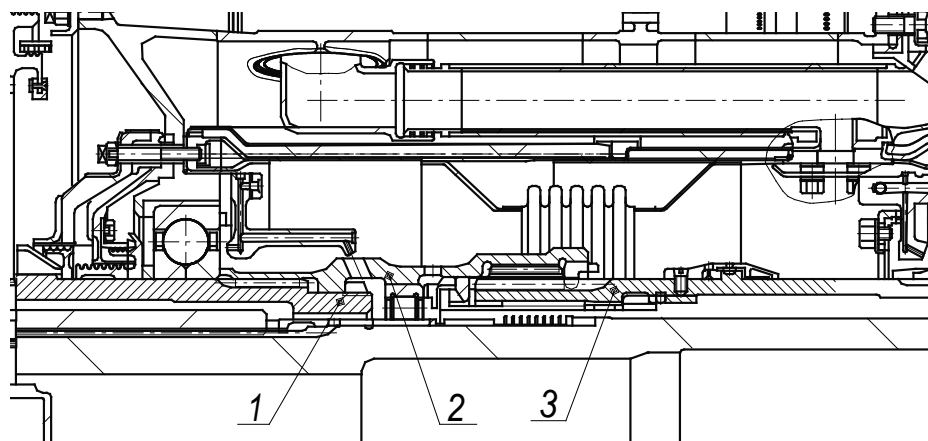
Соединение ротора компрессора и турбины ВД шлицевой муфтой в ТРДД ПС-90А: 1 – вал ротора компрессора ВД; 2- соединительная шлицевая муфта; 3 – вал ротора турбины ВД
